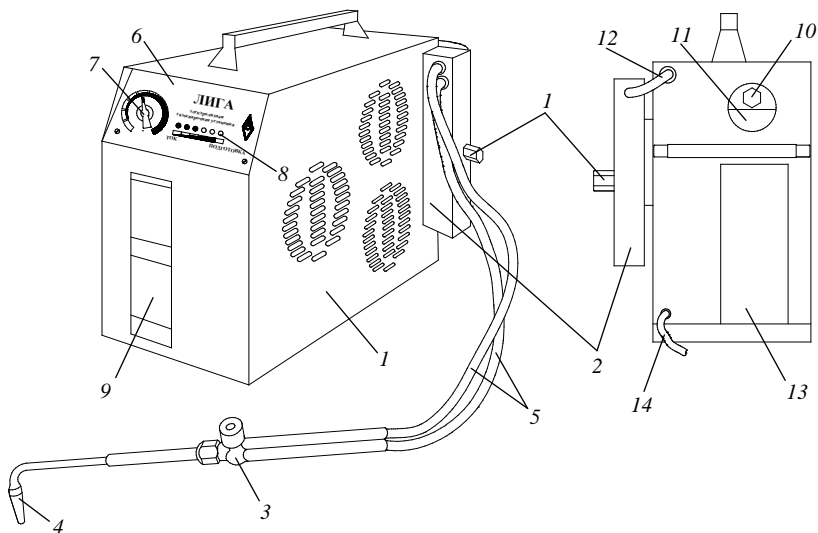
Внешний вид электролизной газосварочной установки «Лига-41»:
